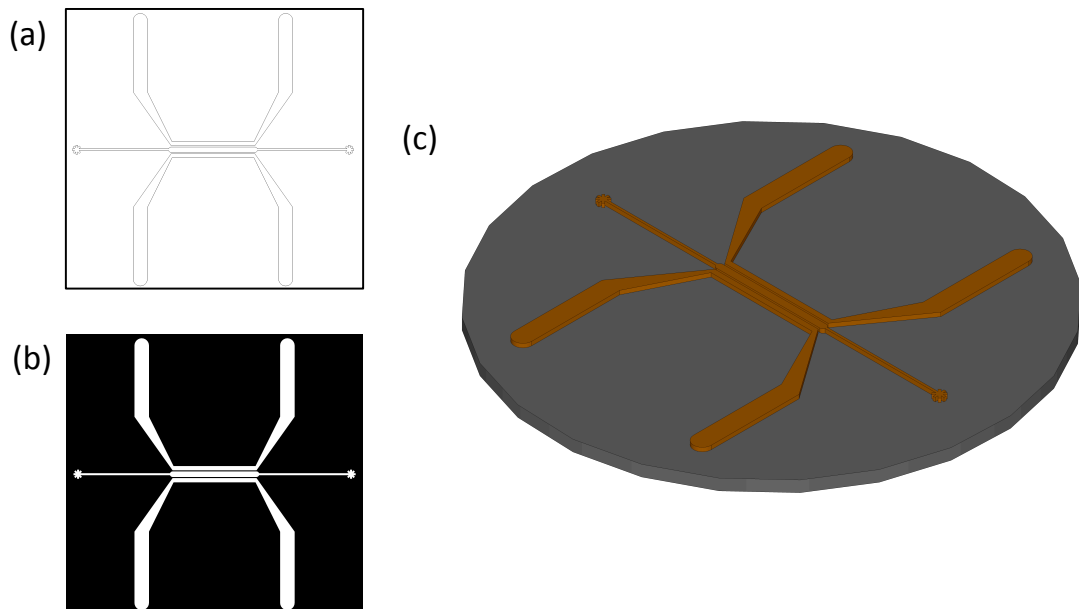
disegno CAD del dispositivo (a); maschera fotolitografica (b) e master mold (c).
